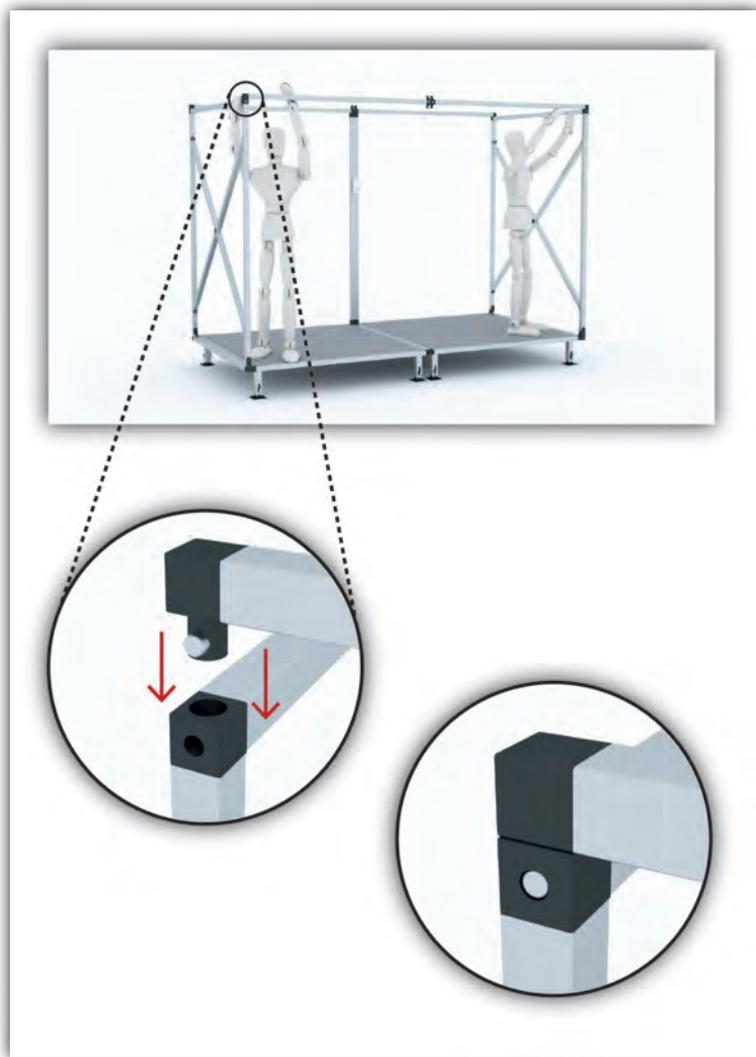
Ensamblaje de largueros intermedios con muros por medio de barril conector en parte media y ensamblaje con esquinas superiores de los muros.
